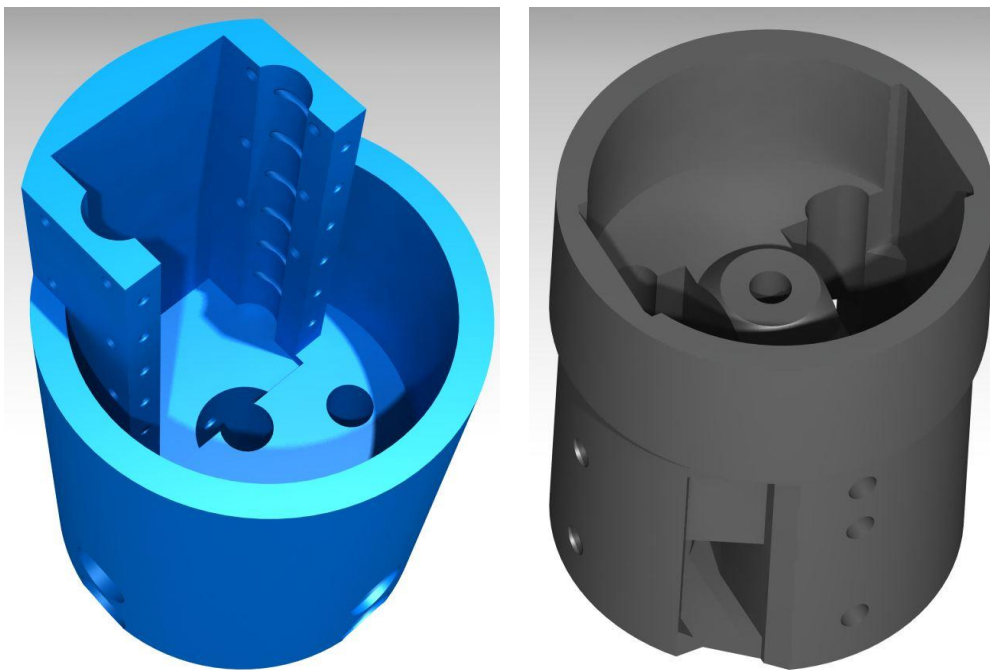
(Izquierda) primera versión del sistema de impulsión con un solo motor y contrapesas regulables para equilibrado basadas en tornillos y arandelas. (derecha) última versión, simétrica, más corta con dos motores para su impulsión.
